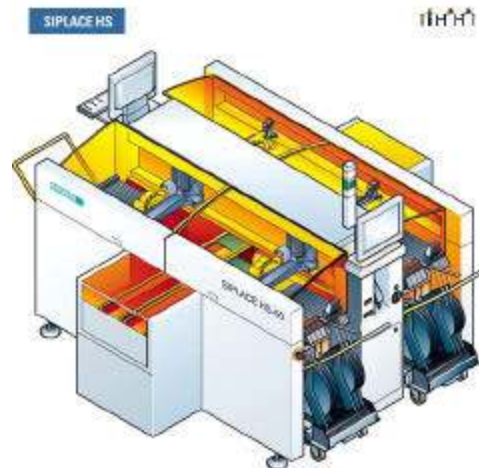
Exemplo de Máquina de Compôr Componentes SMT
